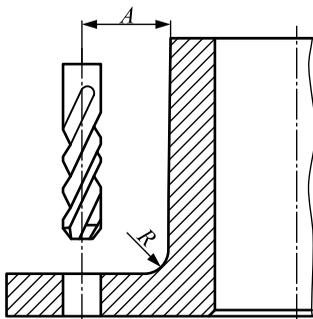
Требования к технологичности расположения оси отверстий относительно вертикальной стенки заготовки
